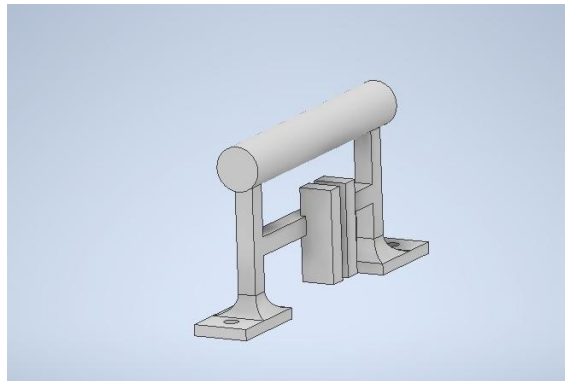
Diseño 3D de la pieza "Eje" en Autodesk.
